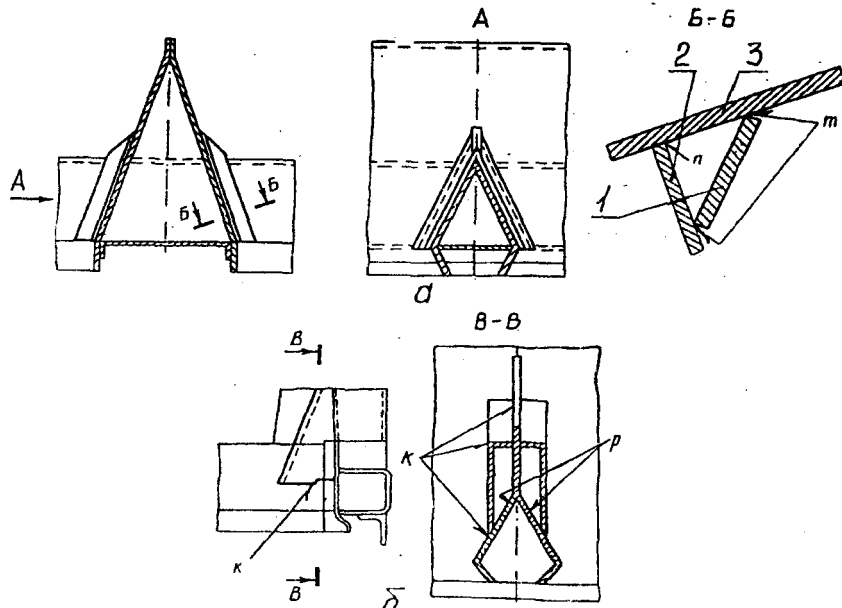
Усиливающие накладки на продольной балке (а) и на промежуточных балках (б)
